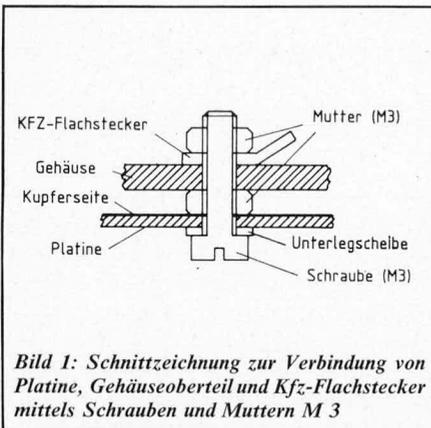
Schnittzeichnung zur Verbindung von Platine, Gehäuseoberteil und Kfz-Flachstecker mittels Schrauben und Muttern M 3
